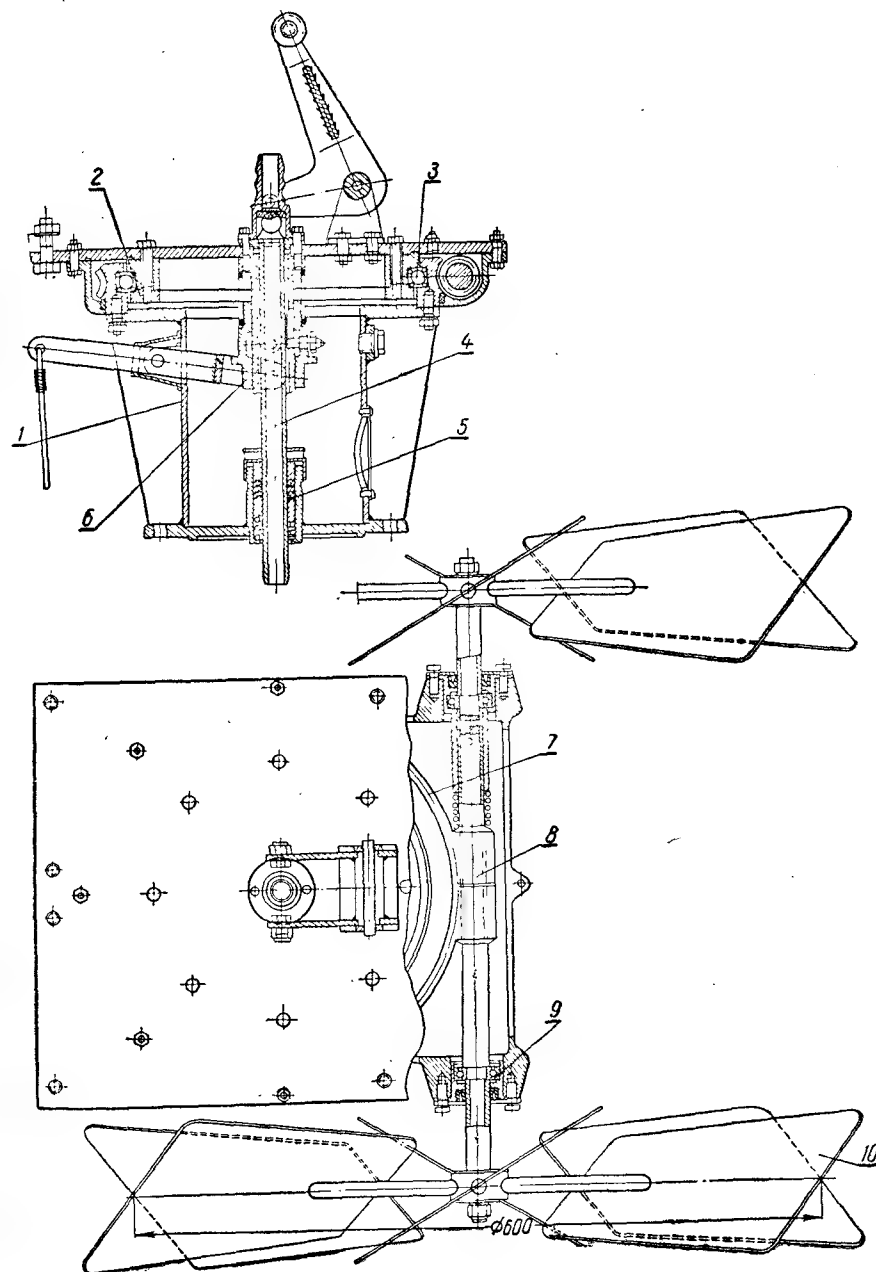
Поворотная опора агрегата «Вихрь» (ВНП-4М):
